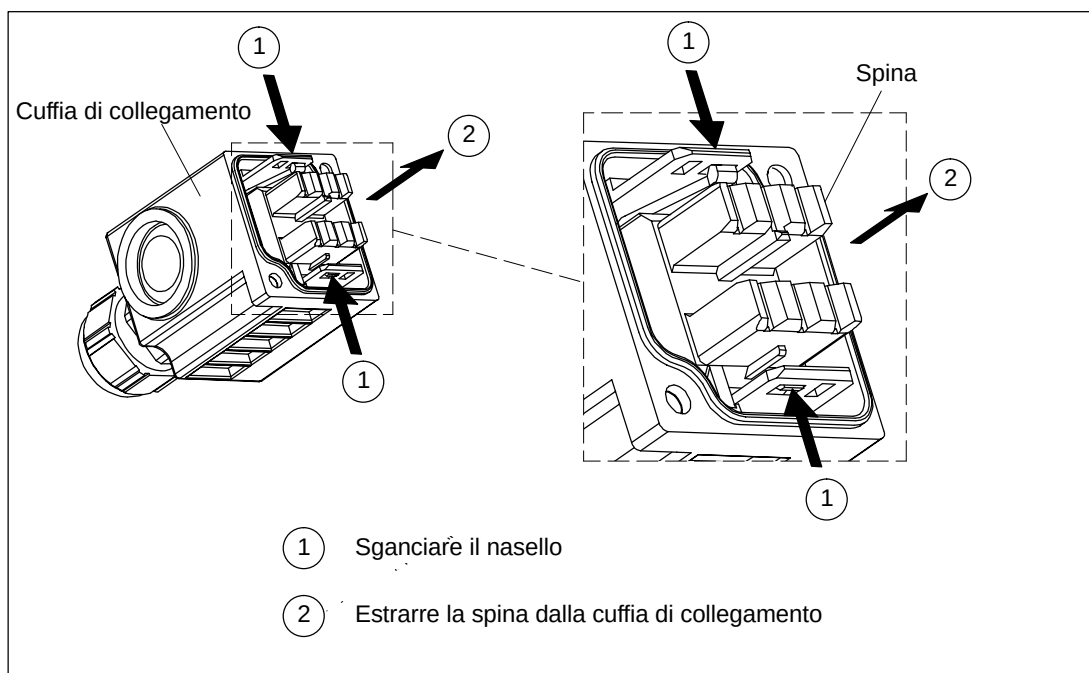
Estrarre la spina dalla cuffia di collegamento
